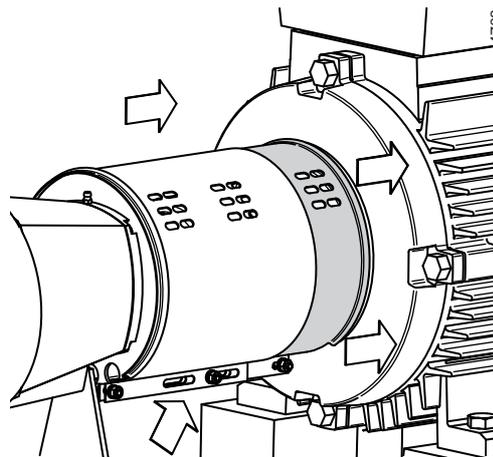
Einstellen des Mantels auf der Motorseite.
